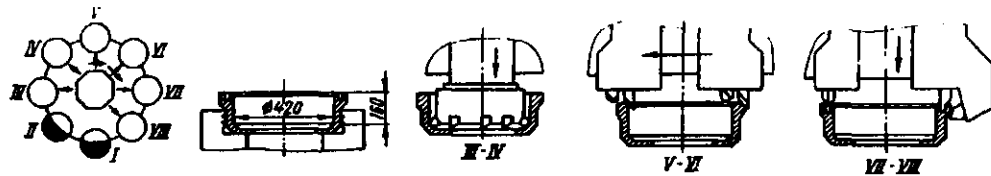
Групповая наладка восьмишпиндельного полуавтомата для обработки тормозных барабанов двух размеров
